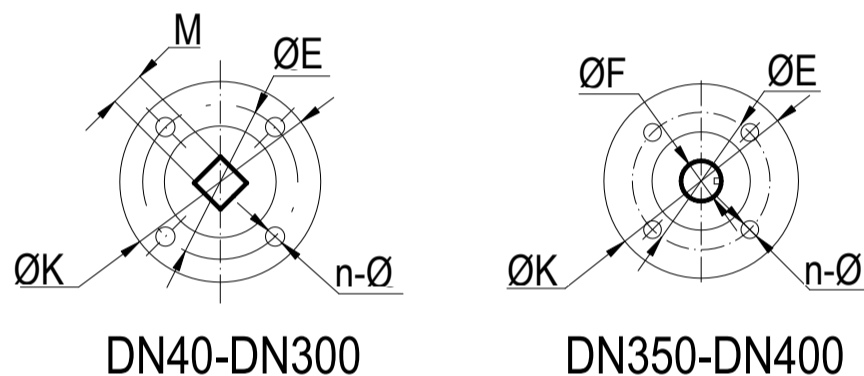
Wymiary podstawowe, na czarno zaznaczono otwory gwintowane | Basic dimensions, marked in black holes mark threaded holes | Размеры основной черной выбран резьбовые отверстия
